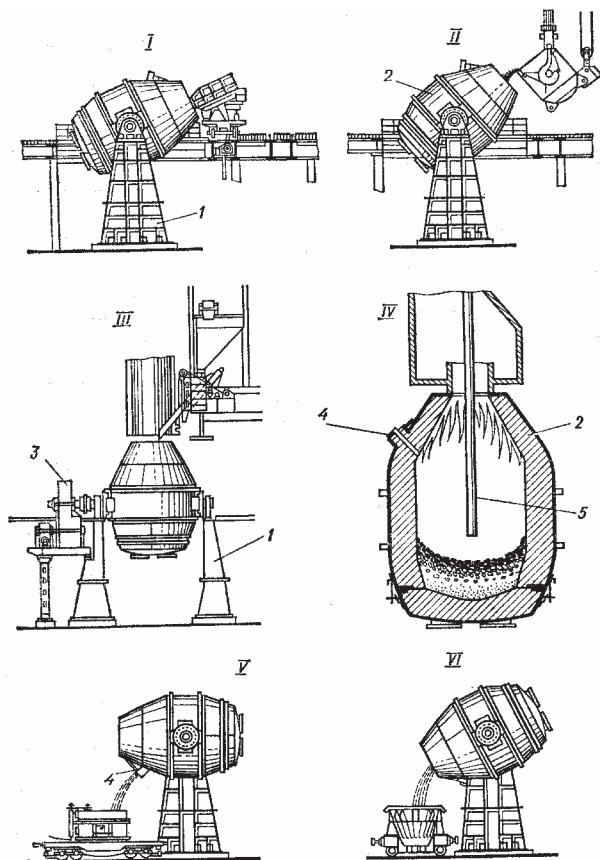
Схема устройства кислородного конвертора и стадии выплавки стали: I – завалка лома; II – заливка чугуна; III – загрузка флюса; IV – продувка конвертора кислородом; V – выпуск стали; VI – слив шлака; 1 – станина; 2 – конвертор; 3 – поворотные цапфы; 4 – отверстия для выпуска стали; 5 – водоохлаждаемая фурма для подачи кислорода
